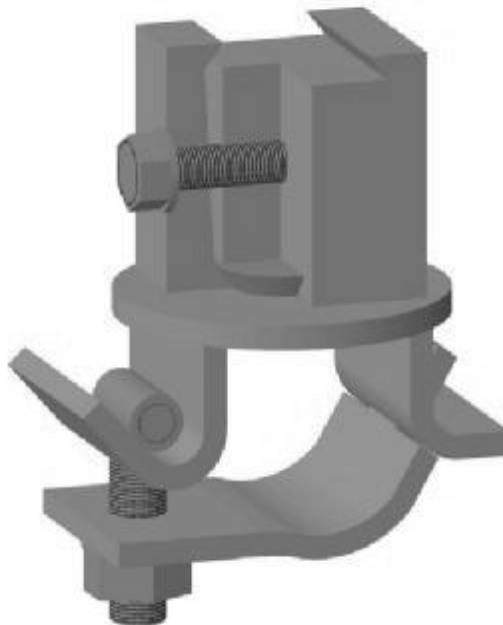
Конусный шарнир с прижимным винтовым приспособлением
